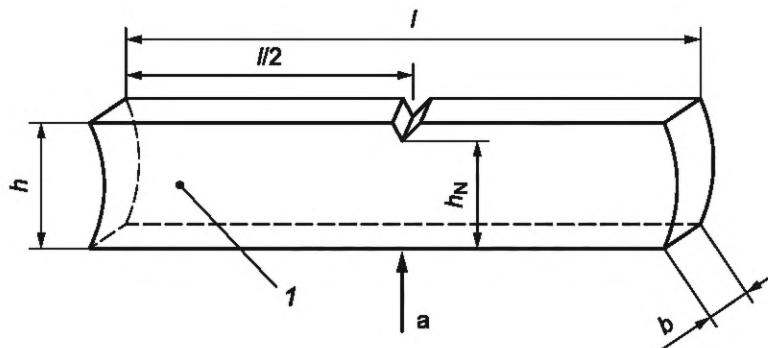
Удар по Шарпи плашмя образца типа 6
